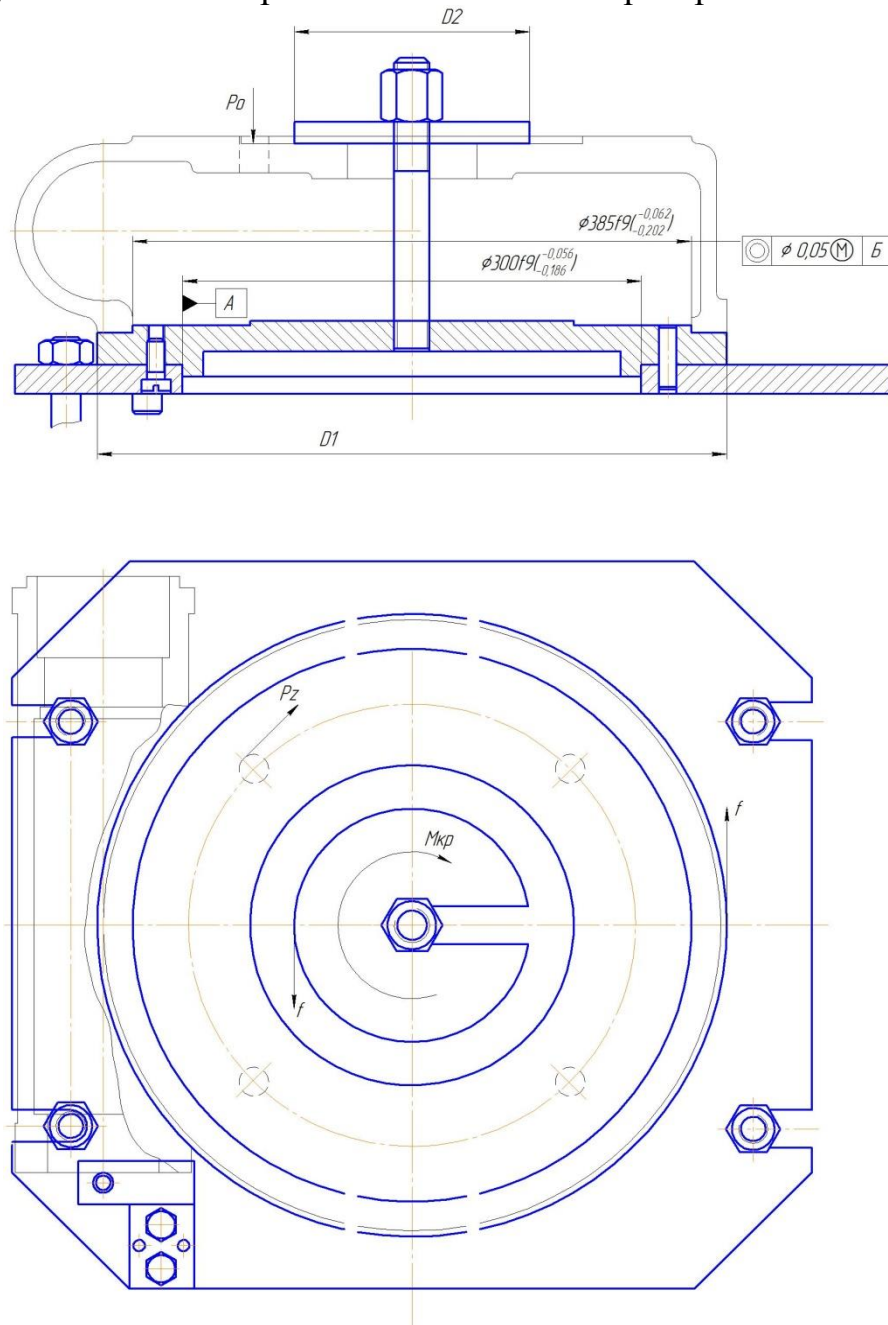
Схема закріплення корпусу НПО- 10.07.201962 в пристрої на вертикально-свердильному верстаті 2Р135Ф2-1.
